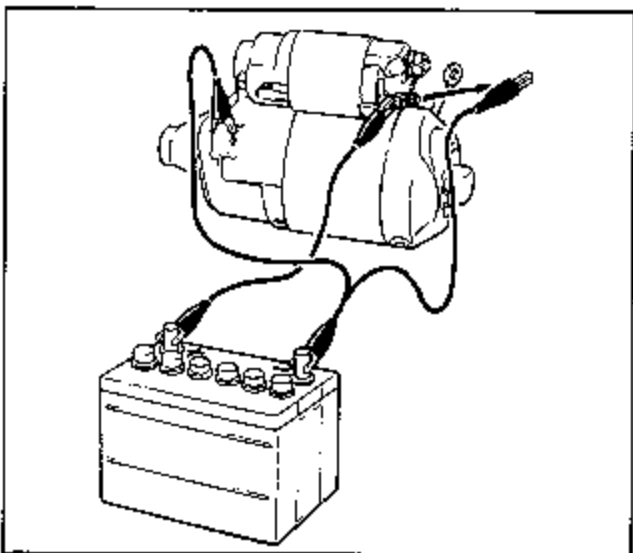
G-29 Revisión de la Bobina de Mantenimiento
